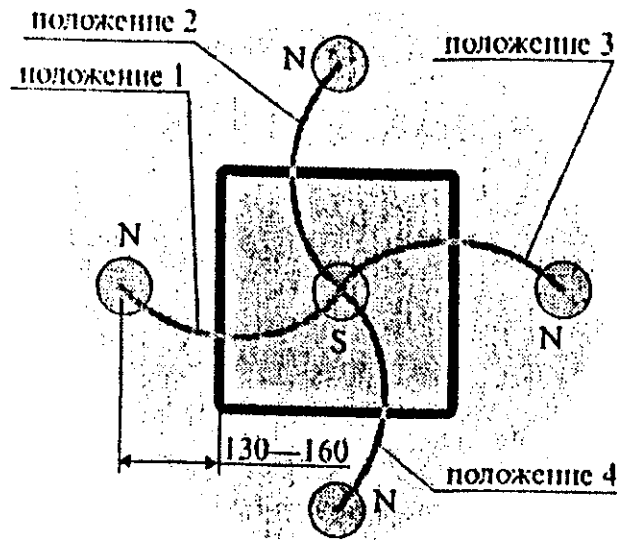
Контроль сварных швов накладки с размерами сторон (200—300) мм
